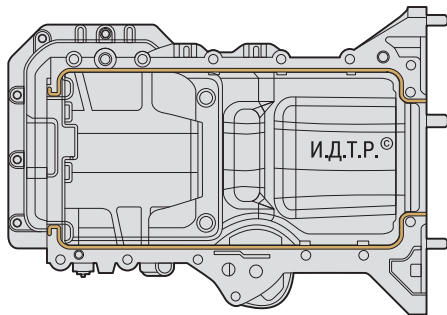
Схема нанесения герметика на привалочную поверхность блока цилиндров
